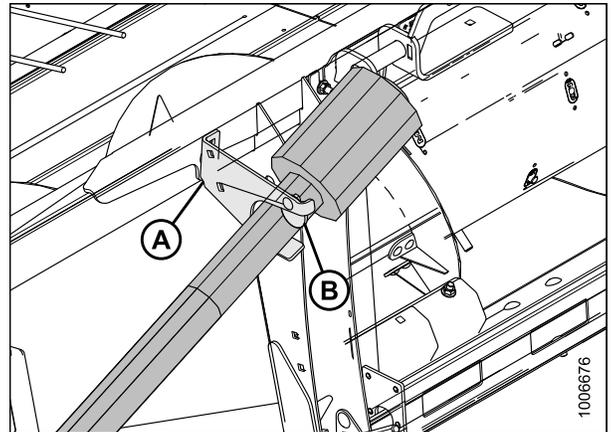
Extremo de la cosechadora del cardán en posición de almacenamiento
